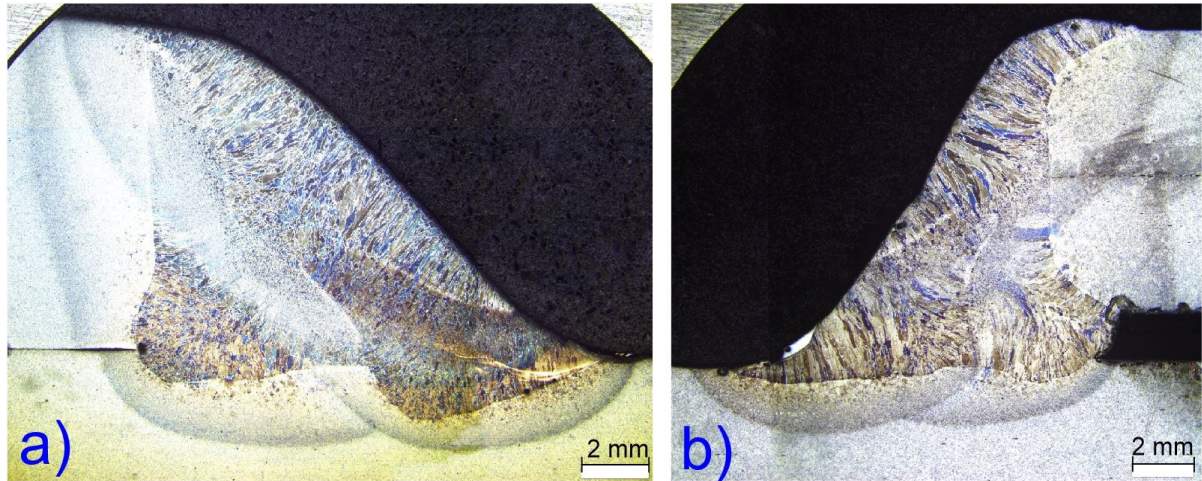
Macrografias da soldagem de dupla-calha com aquecimento duplo Calha/Tubo. Em a) GMAW-P; b) GMAW-PAC.
